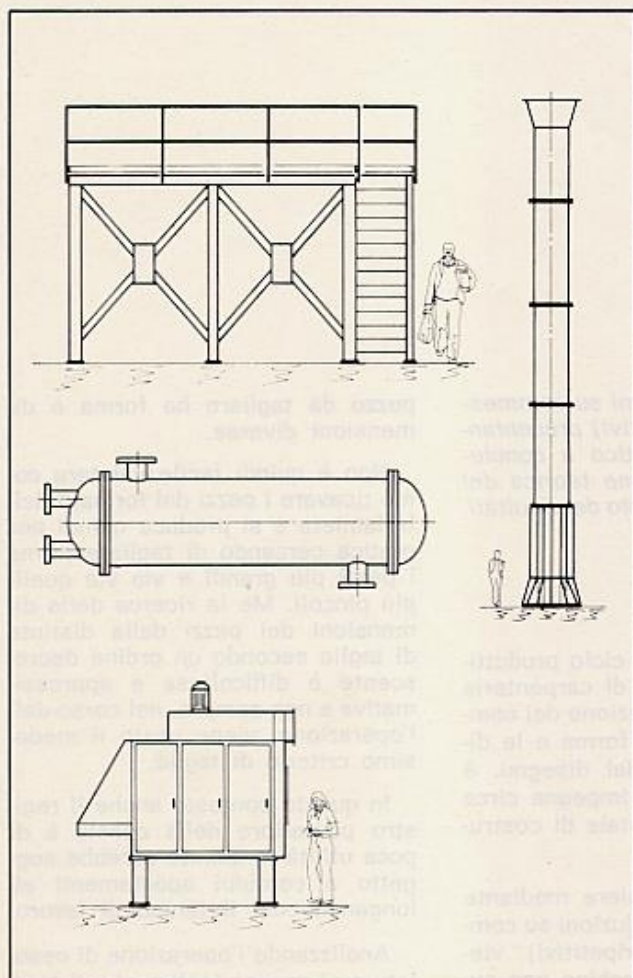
Manufatti elettrosaldati in lamiera e profilati d'acciaio.
